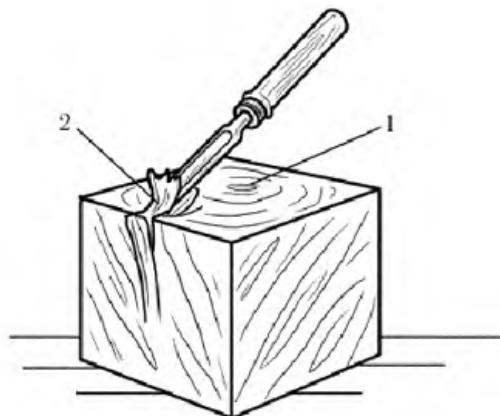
Выполнение среза на торцевой плоскости заготовки
